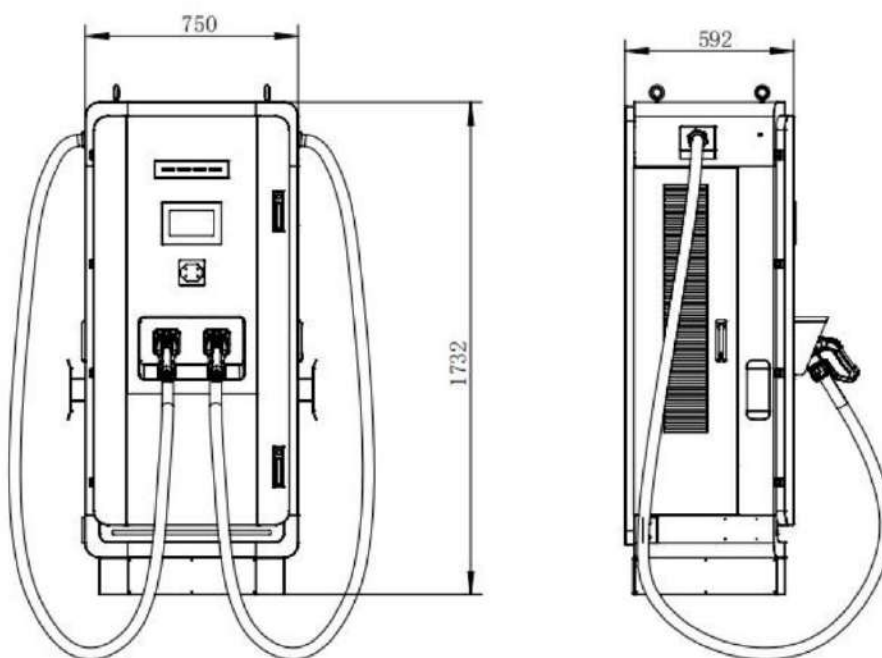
Dimensiones del equipo (MDDC-120kW/160kW)
